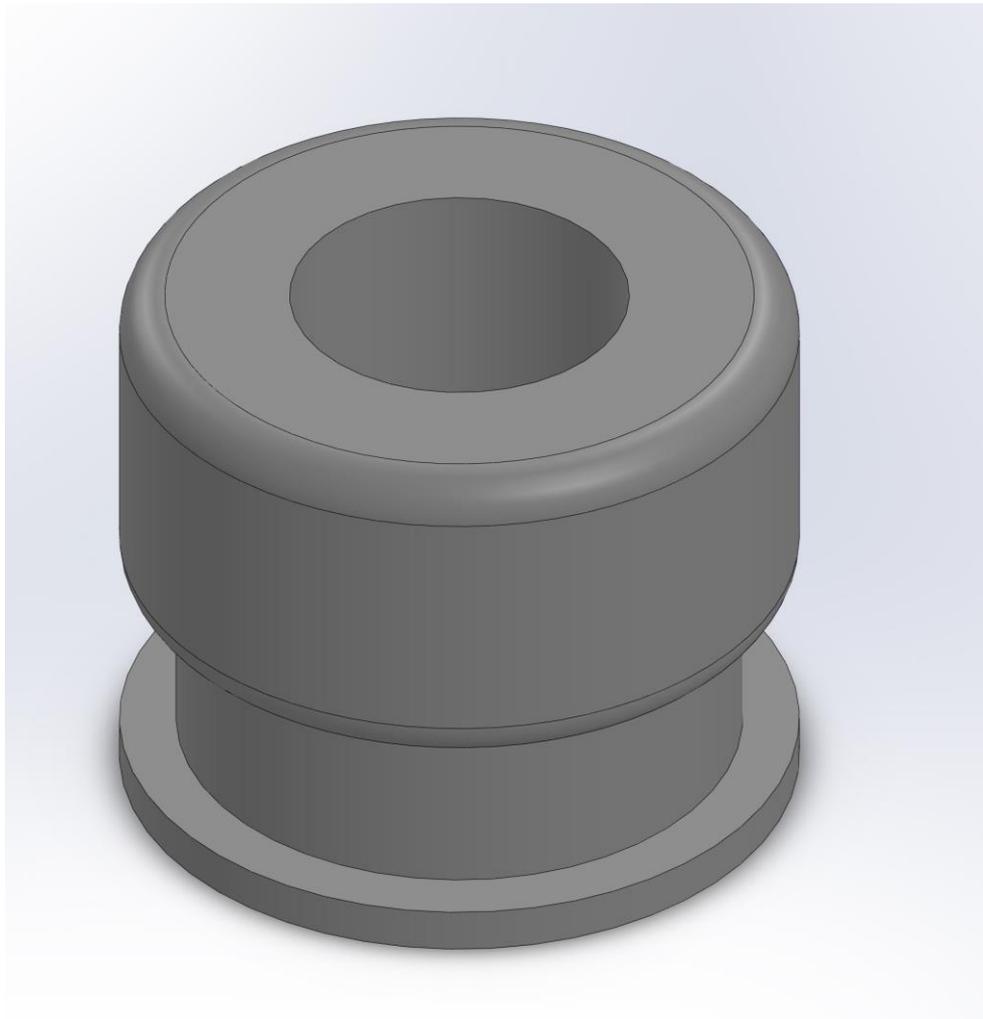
Modelagem do encaixe para haste. Fonte: Elaboração própria
